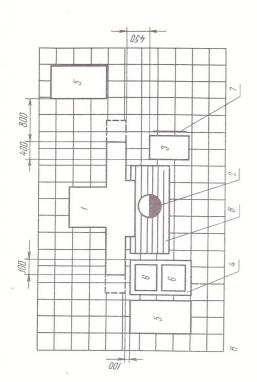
Рабочее место шлифовальцика: в) I- плоскошлифовальный станок; 2- шлифовщик; 3- тумбочка инструментальная двухсекционная С3746.05; 4- стол производственный С3702.51; 5- стеллаж-подставка СД3702.10A; 6- тара производственная; 7- планшет для чертежей СД3750.04; 8- решетка под ноги рабочему
